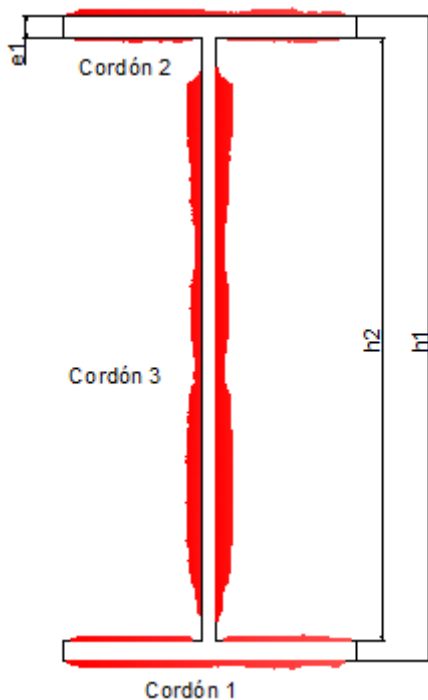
Cordones de soldadura expuestos en el perfil
